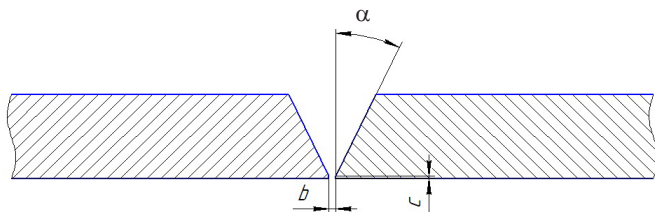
Параметры подготовки и сборки свариваемых пластин:
